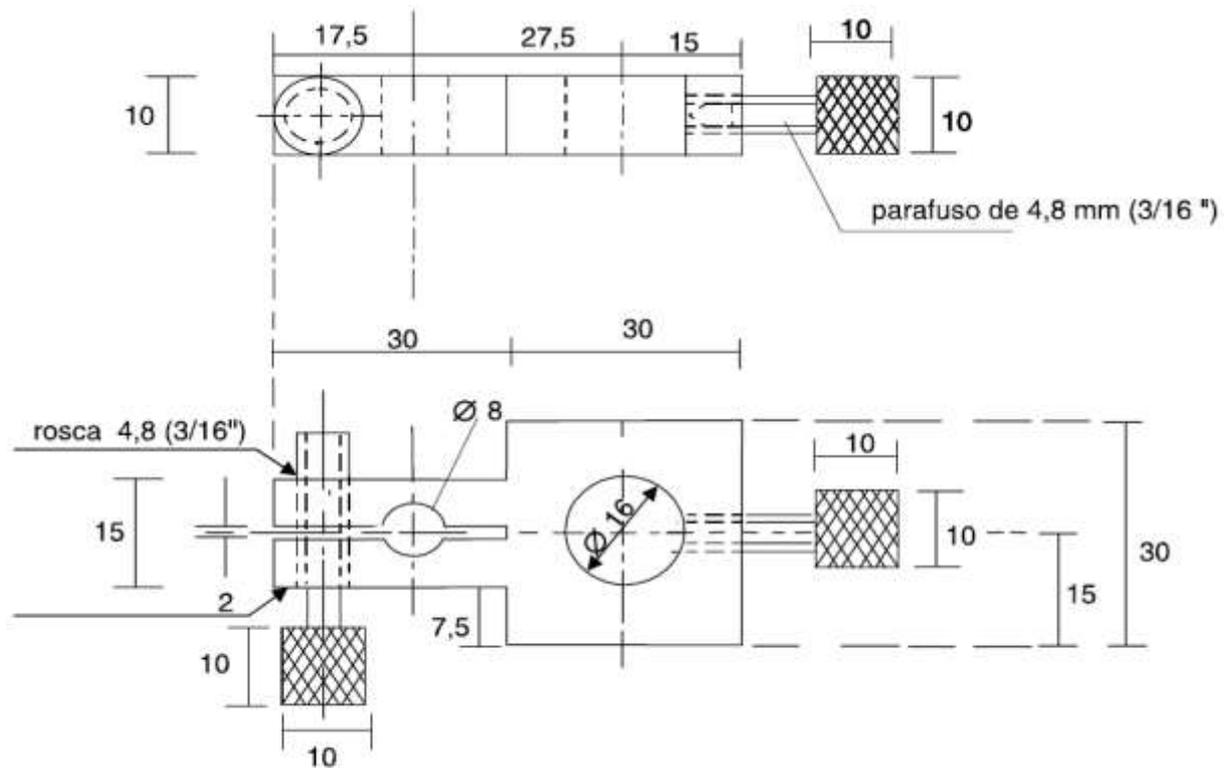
Suporte do extensômetro (dimensões em milímetros)
